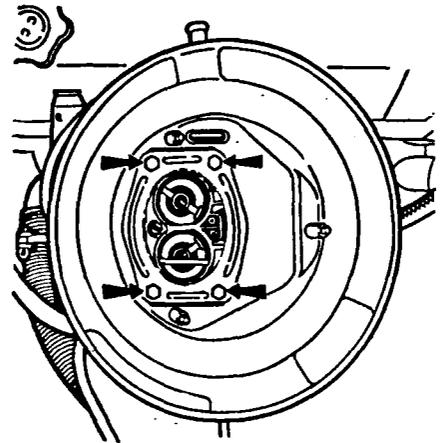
Снятие воздушного фильтра. Стрелками указаны гайки крепления корпуса фильтра к карбюратору
